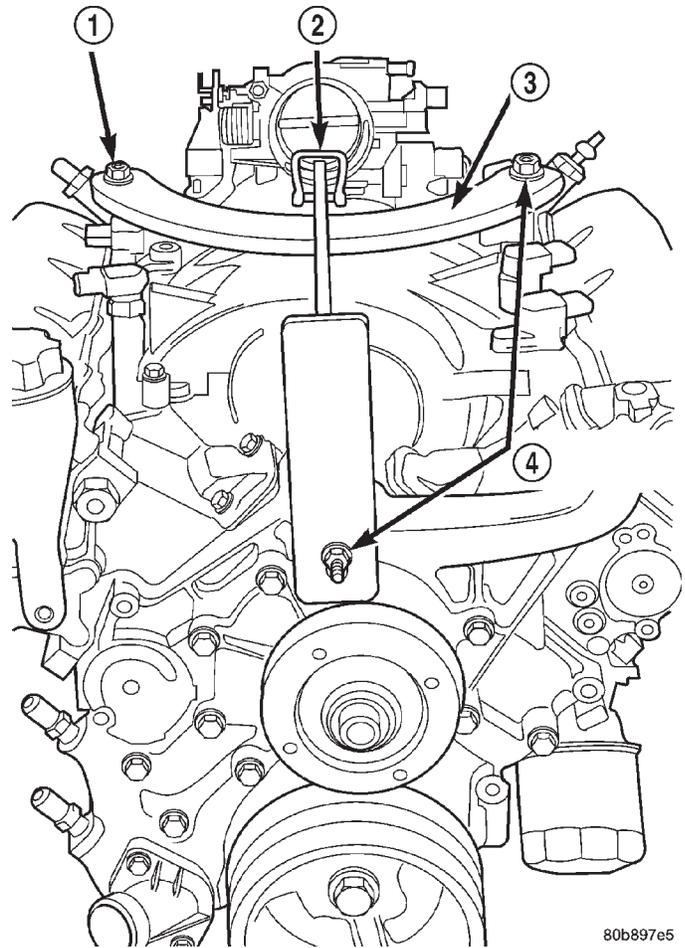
Befestigungspunkte der Motorhebevorrichtung
